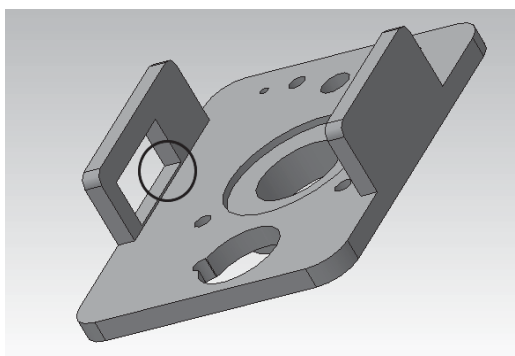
Область, скопления газовых раковин, вскрывающихся при механической обработке.
